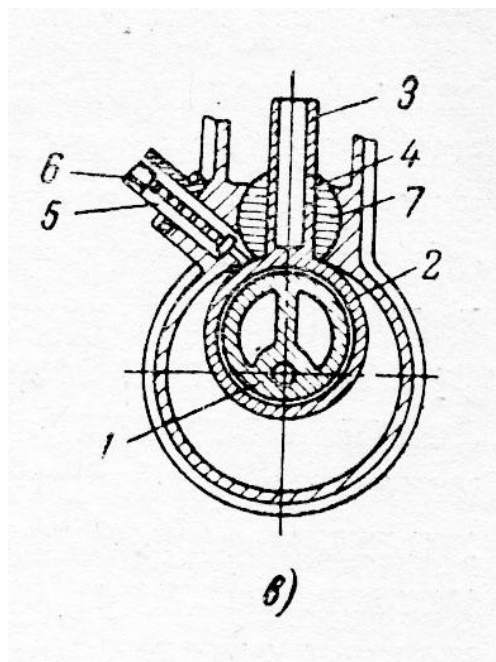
Схема механічного вакуумного насоса: 1 – ротор; 2 – корпус; 3 – золотник; 4– впускний клапан; 5 – випускний патрубок; 6 – клапан; 7 – шарнір золотника
